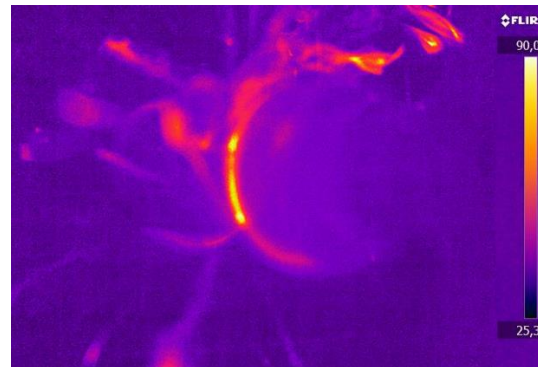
IR-Aufnahme der Bearbeitung von Stahl mit verschlissenen Werkzeug
